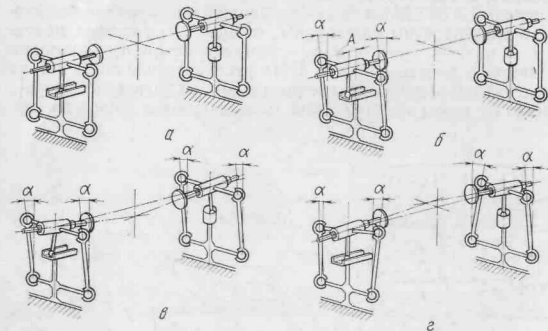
Схема смещения шарнирной системы опор конвертера:
